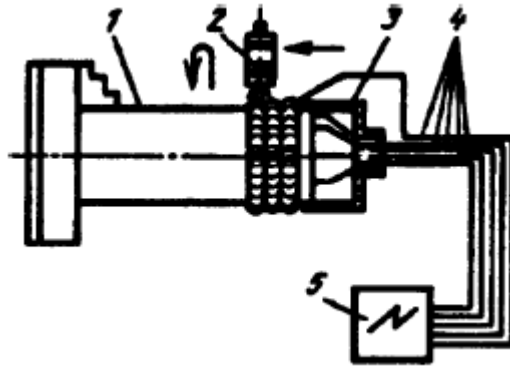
Схема вимірювання температури за товщиною заготовки: 1 – заготовка; 2 – плазмотрон; 3 – захисний екран; 4 – термопар; 5 – осцилограф.
